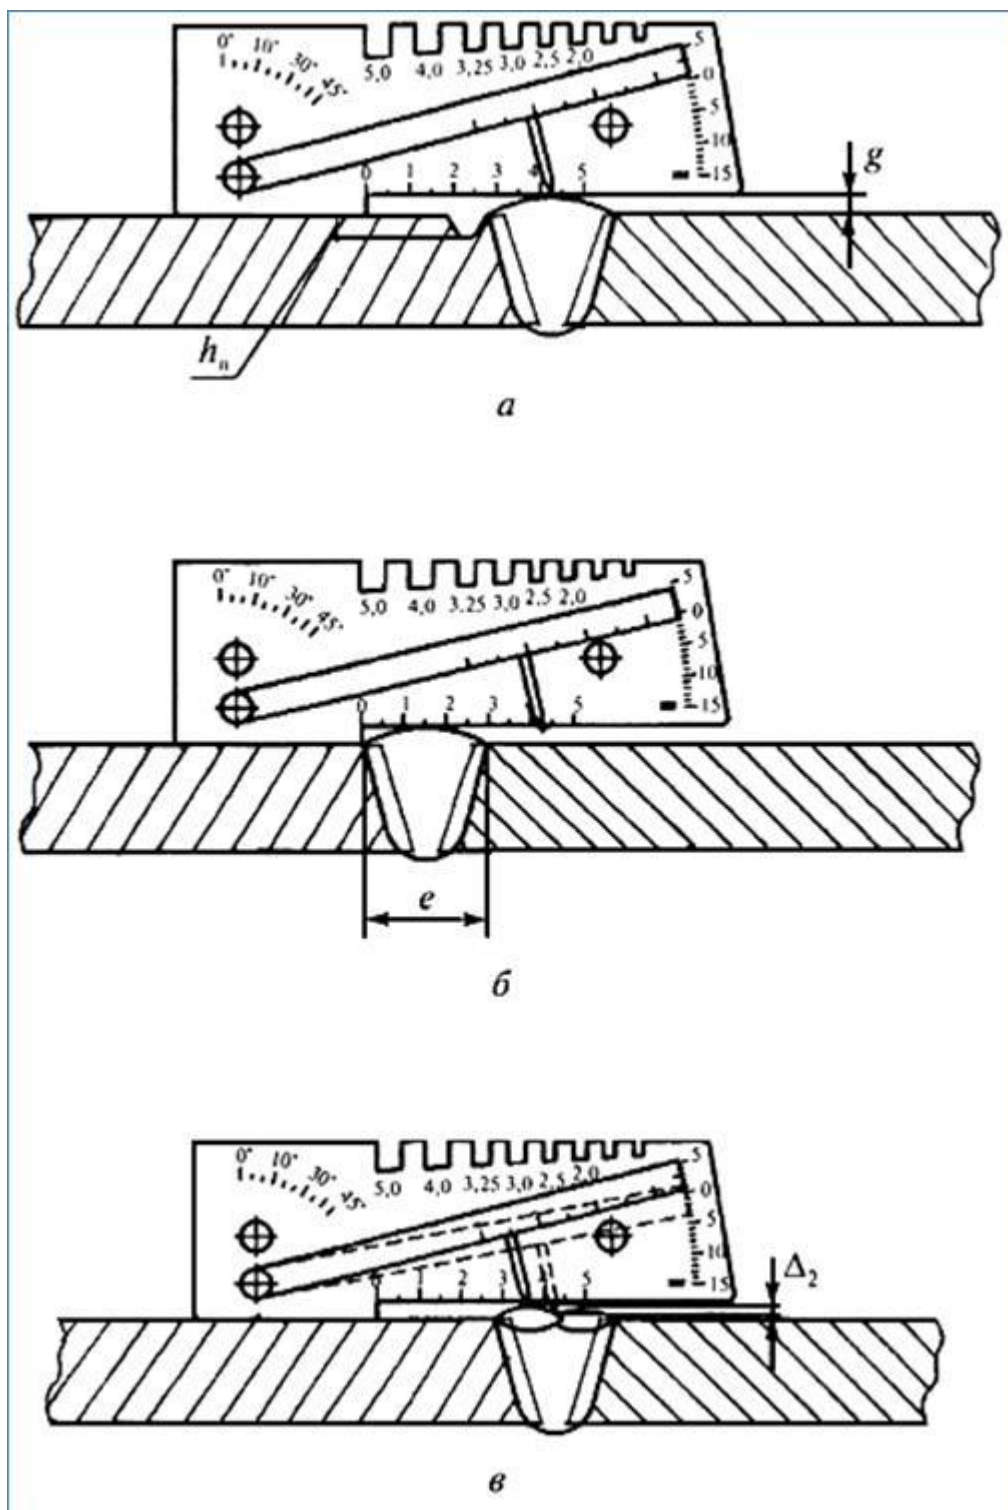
Измерения при помощи УШС-3: а - измерение высоты сварного шва и глубины подреза; б - измерение ширины сварного шва; в - измерение западений между валиками сварных швов
